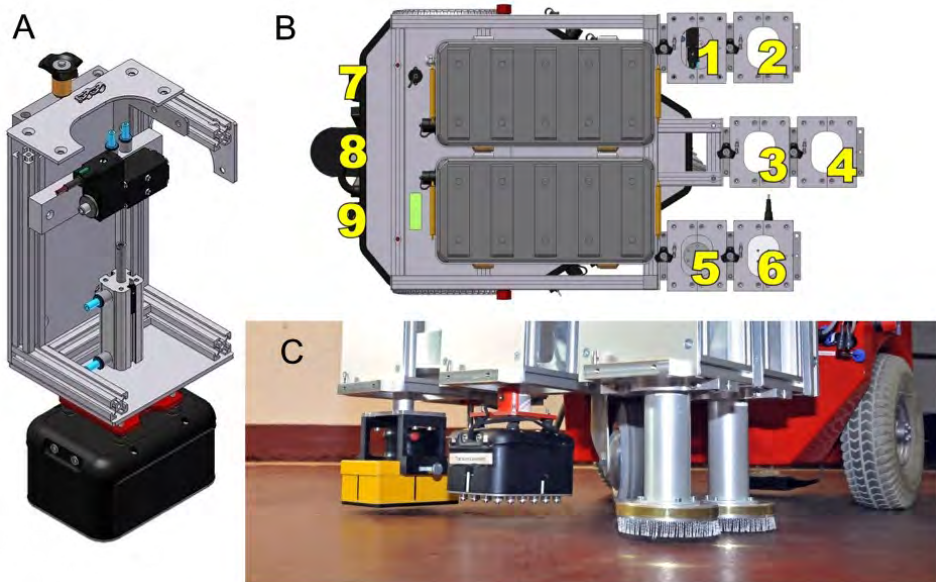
A: Schnitt durch den Entwurf der Standard-Sensorhalterung, hier mit eingebautem pneumatischem Hubzylinder und Ultraschall-Messkopf; B: Draufsicht auf die Roboter-Plattform mit modularer Befestigungsmöglichkeit der Sensorgehäuse an den Positionen 1 bis 6 (gelb), C: Sensorrahmen an der Roboterplattform mit Radarantenne, Ultraschallmesskopf und zwei Mikrowellen-Feuchtesensoren (v.l.nr.)
